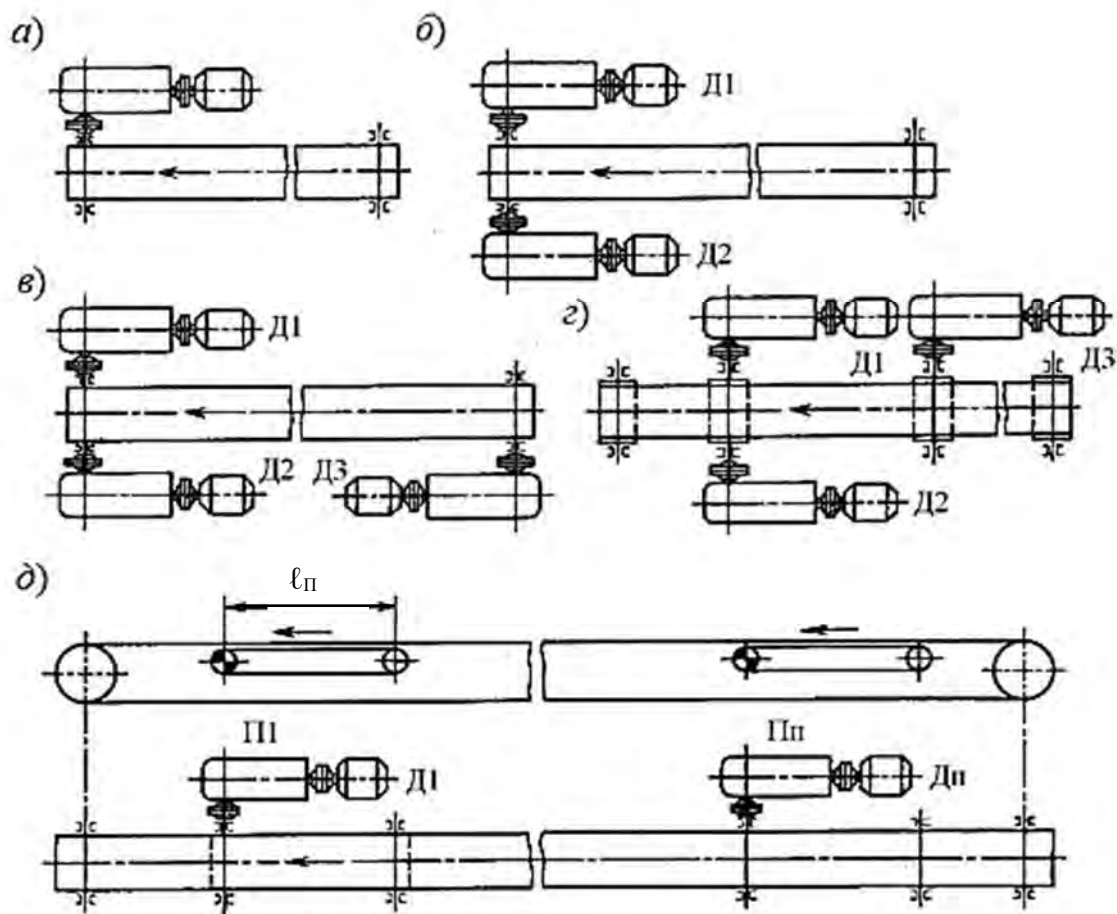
Схемы расположения приводов: а — с одним двигателем; б — с двумя двигателями; в, г — с тремя двигателями; д — многоприводного с промежуточными приводами
